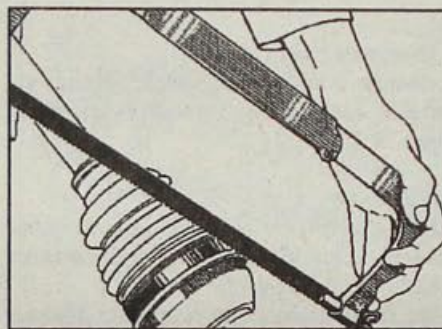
Распиливание хомута крепления защитного чехла к корпусу шарнира
